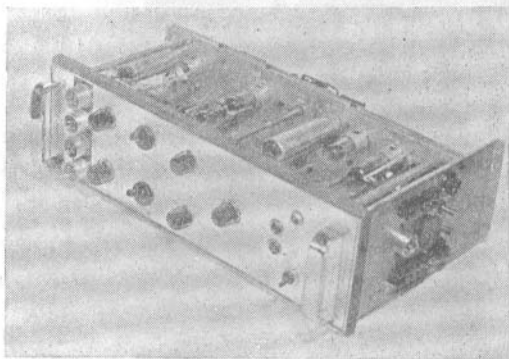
Přístroj se základní kostrou, kolmou k čelnímu panelu
